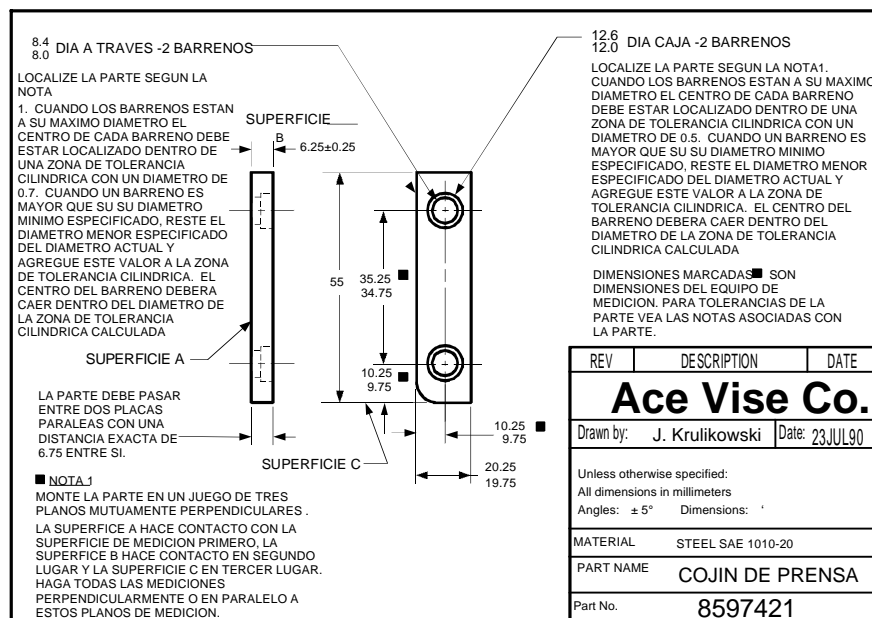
Notas requeridas para que un dibujo con tolerancias por coordenadas tenga la misma información que un dibujo con tolerancias geométricas
